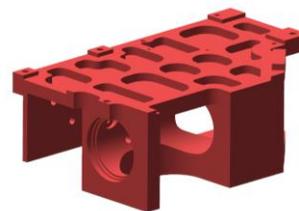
Изготовленный опытный образец кронштейна выверки коллиматора
